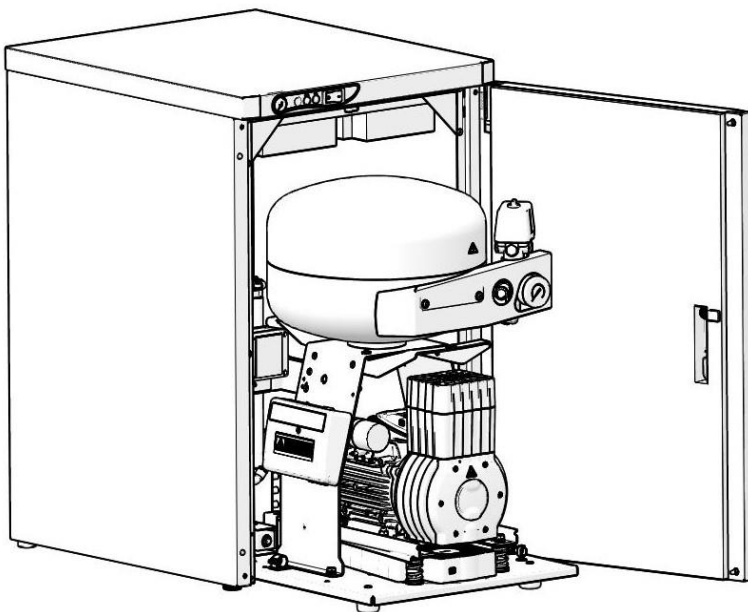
Positionierung des Kompressors für elektrische Anschlüsse
